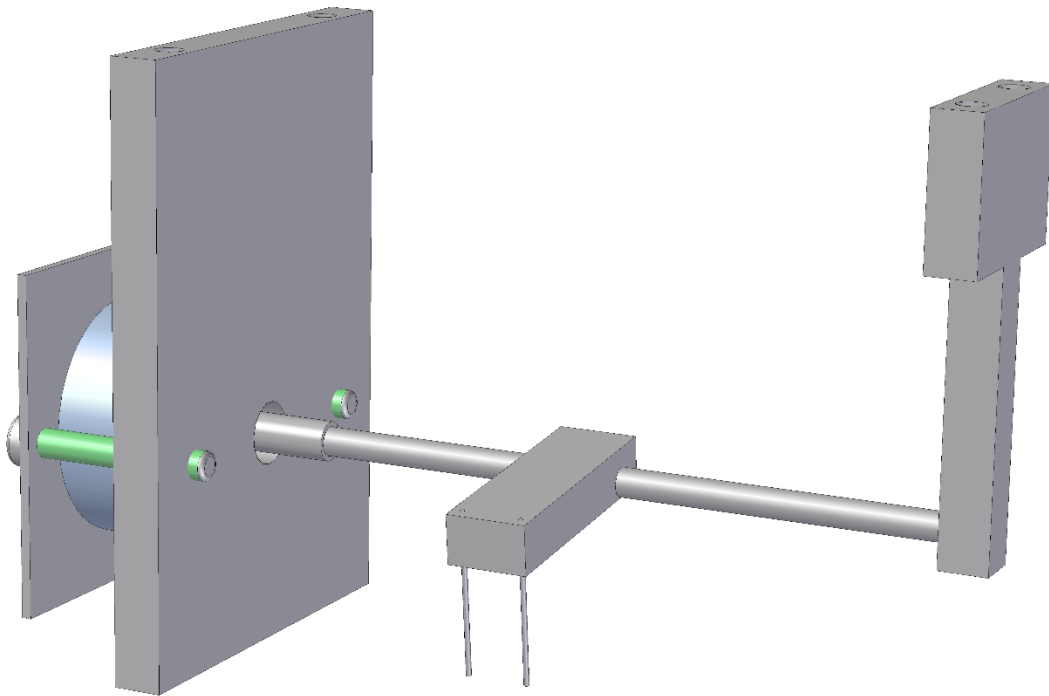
Diseño en Solid Edge del sistema que mantiene la bola impactadora en su posición inicial antes de ser impulsada por la bobina de voz.
